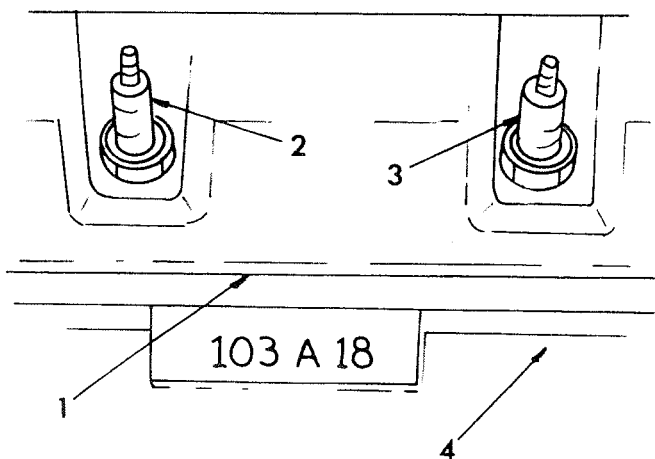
Lage der Motornummer beim Sechszylindermotor.
